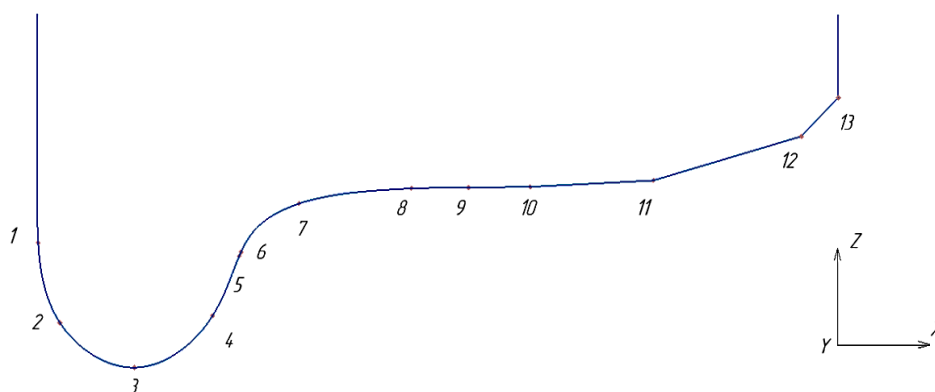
Профиль поверхности катания цельнокатаного колеса
